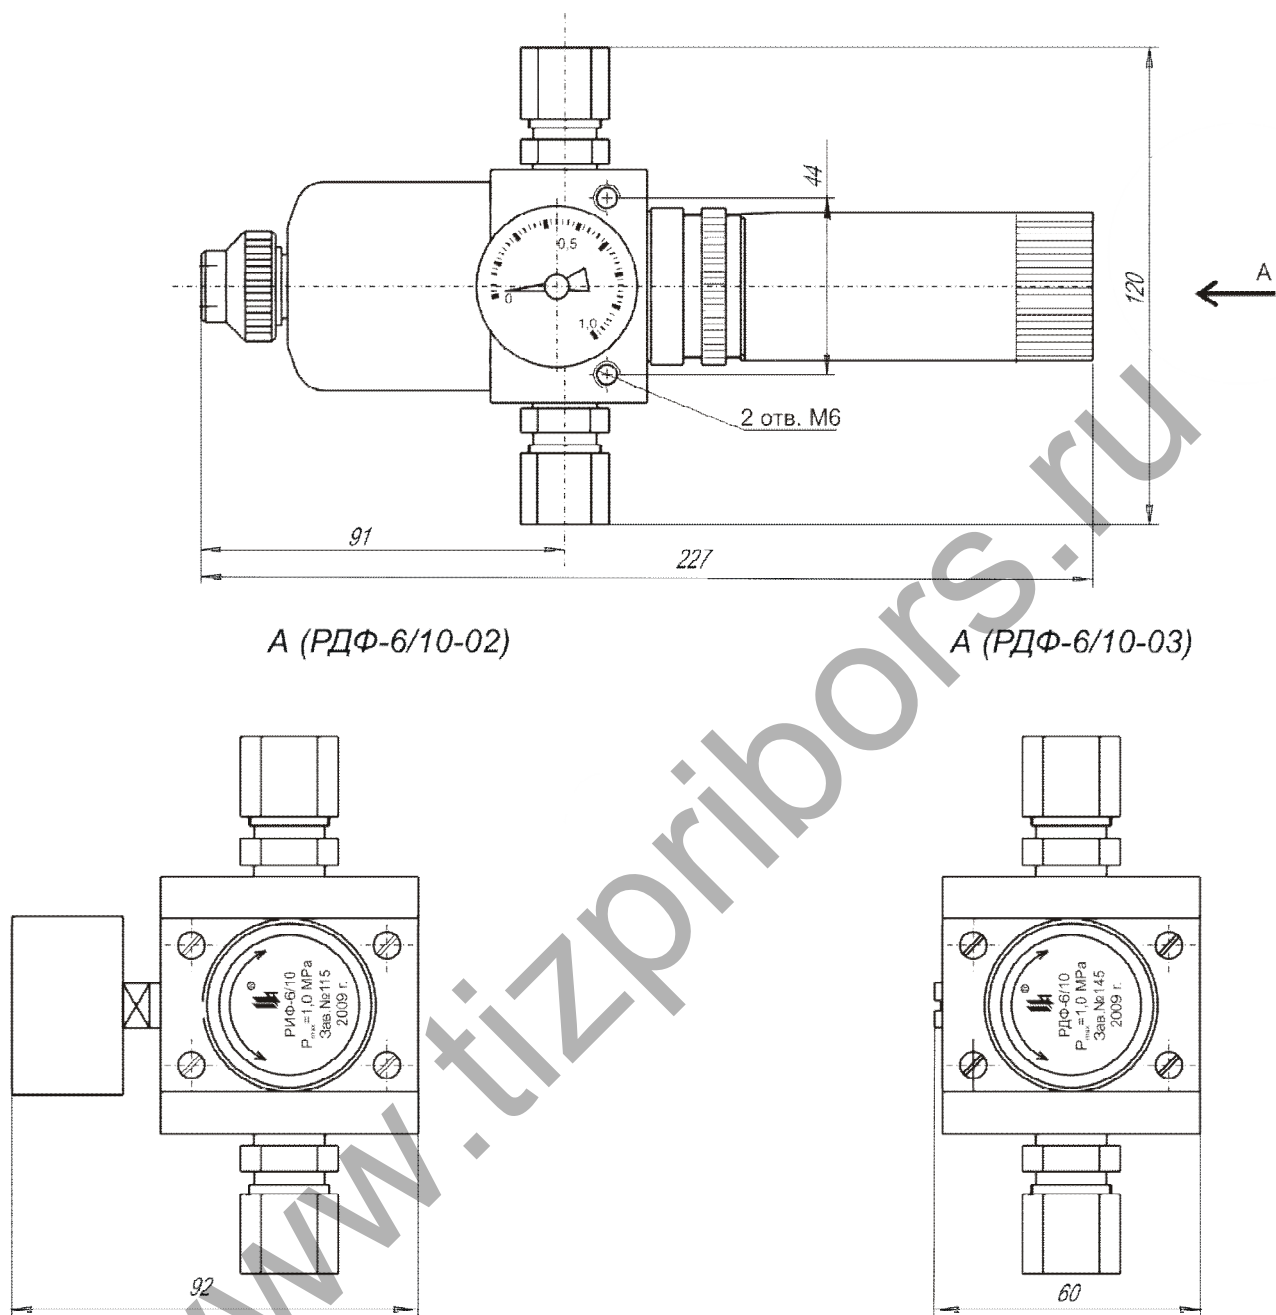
Габаритные и установочные размеры редуктора с верхним пределом регулируемого давления 1,0 МПа
